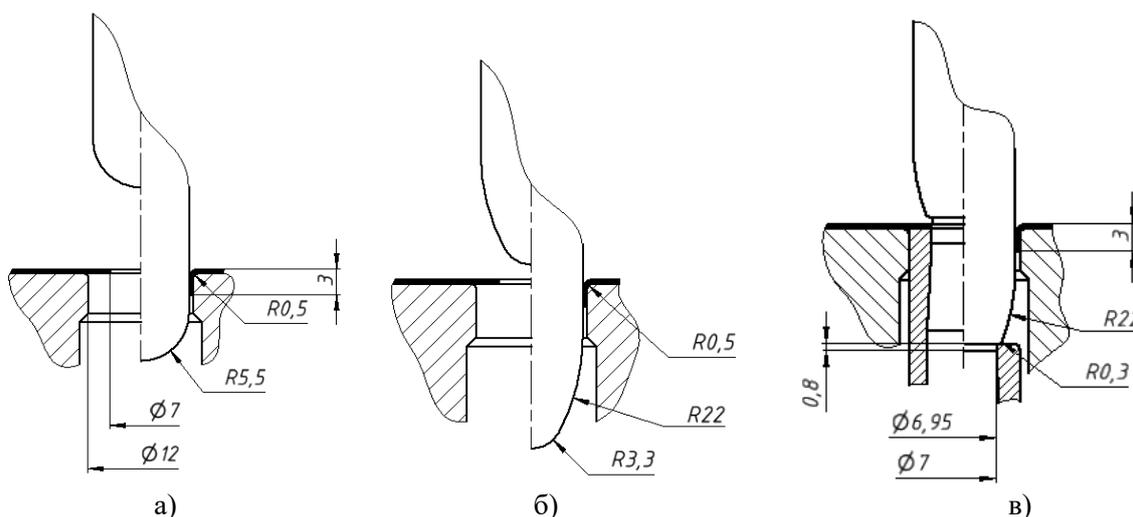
Варианты конструкций пуансонов: а) сферический пуансон; б) криволинейный пуансон; в) комбинированный пуансон с криволинейной образующей и пробивной кромкой
